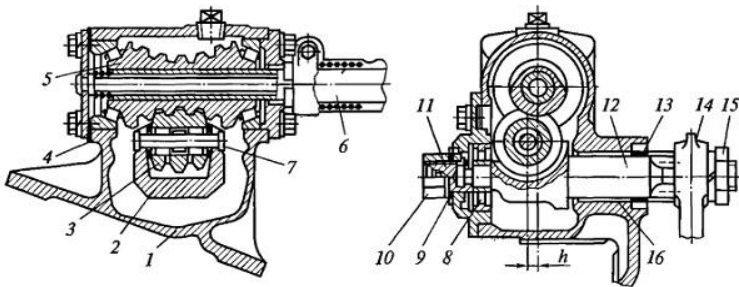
Рульовий механізм типу «глобоїдний черв'як – ролик» (1-картер рульового механізму; 2-головка валу рульової сошки; 3-тригребневий ролик; 4-прокладки для регулювання; 5- черв'як; 6-рульовий вал; 7-вісь; 8-підшипник валу сошки; 9-стопорна шайба; 10-ковпачкова гайка; 11-регулювальний гвинт; 12-вал сошки; 13-сальник; 14-рульова сошка; 15-гайка; 16-бронзова втулка; h -глибина зачеплення ролика з черв'яком, що регулюється).
